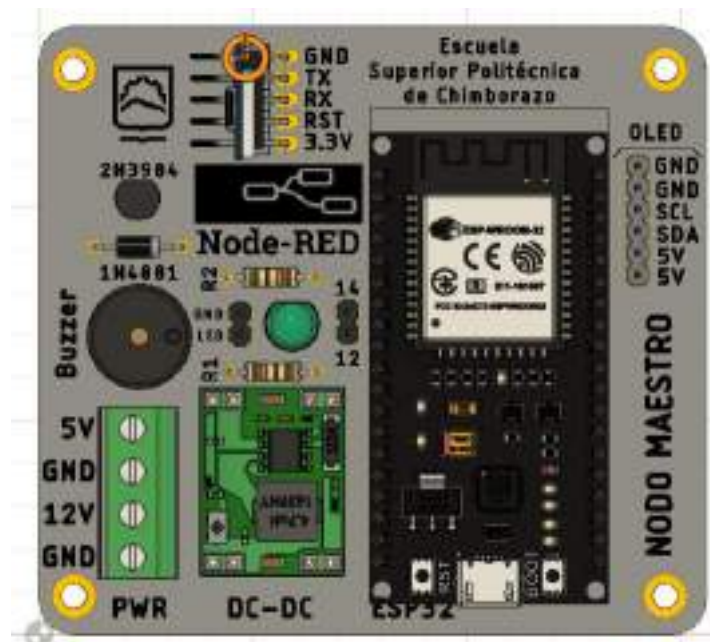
Diseño de placa PCB en 3D del nodo maestro
